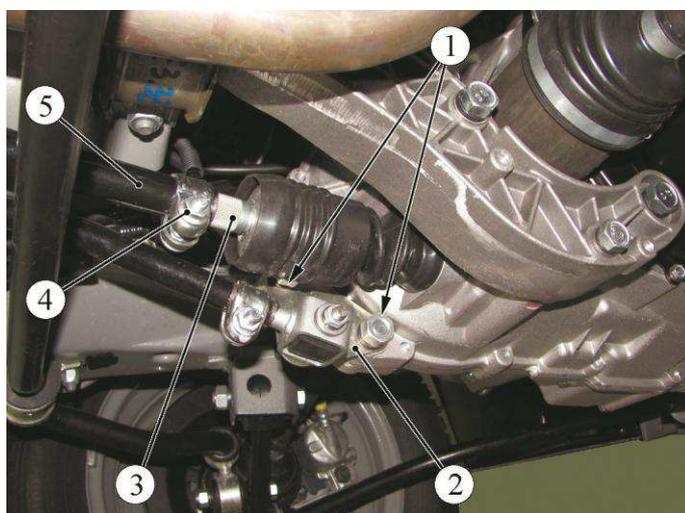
Отсоединение реактивной тяги и тяги привода коробки передач:
